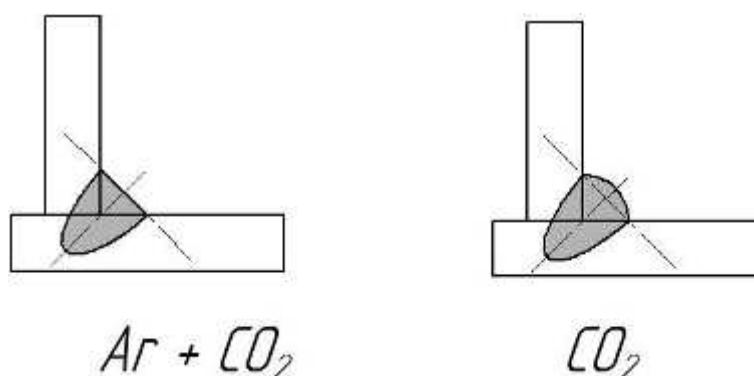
Форма шва при сварки в СГОА и CO_2
